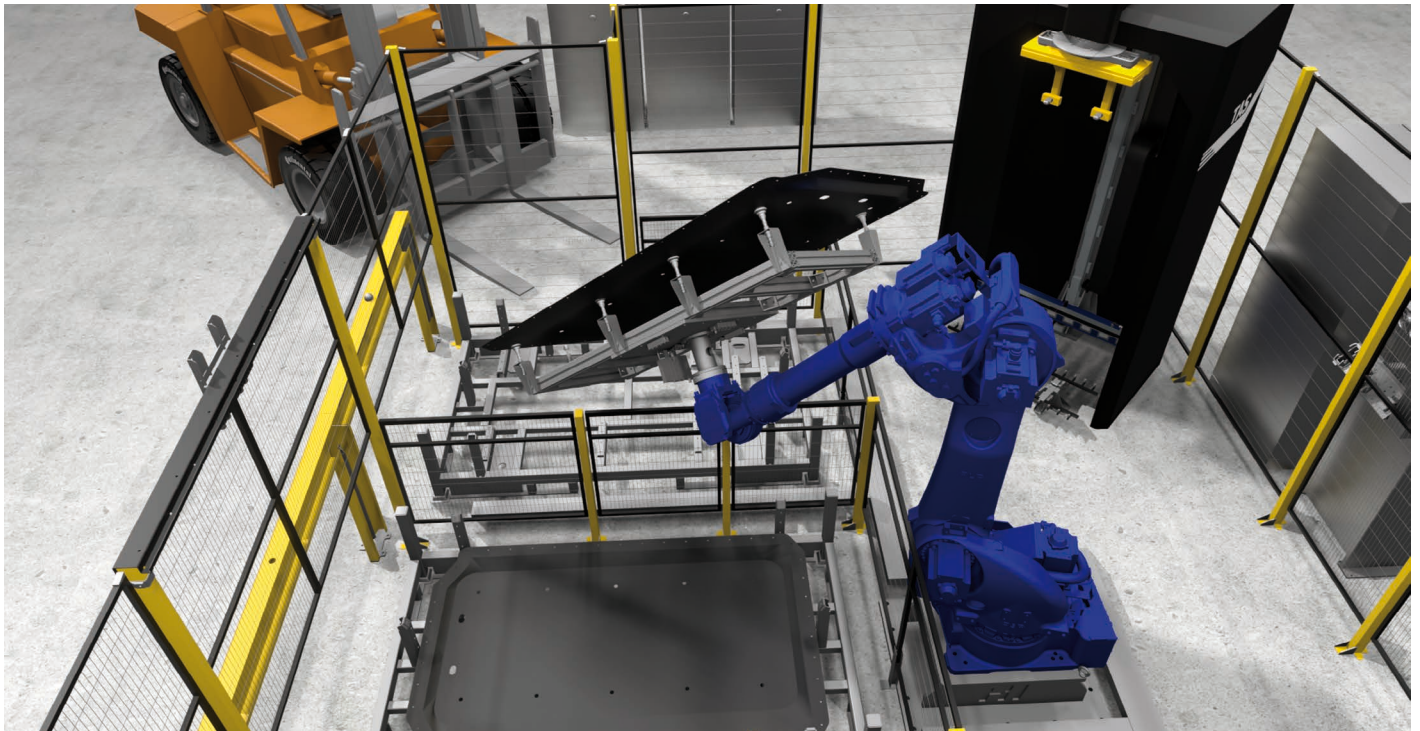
Ein Zulieferer der Automobilindustrie konnte mithilfe Deep-Learning-gestützter Machine Vision die visuelle Inspektion von Batterieklappen für Elektrofahrzeuge deutlich optimieren.
